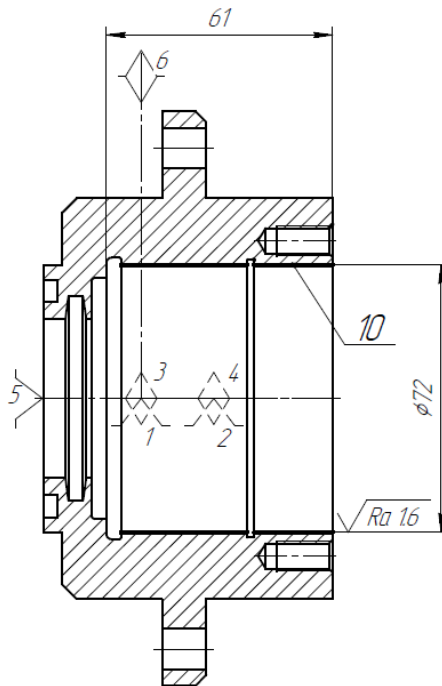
Схема базування та ескізи обробки на операцію 050
